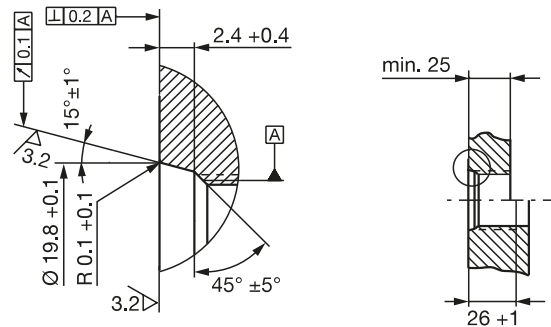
Einschraubloch M18x1.5 nach ISO 6149 O-Ring 15.4x2.1
